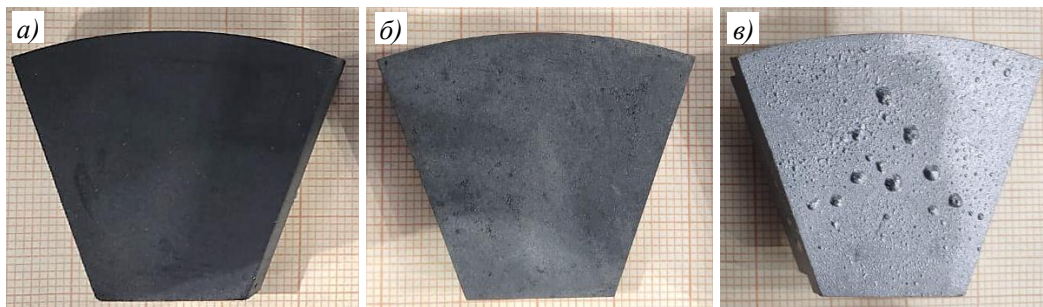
Внешний вид заготовки типа 1 после прессования (а), карбонизации (б) и силицирования (в)
